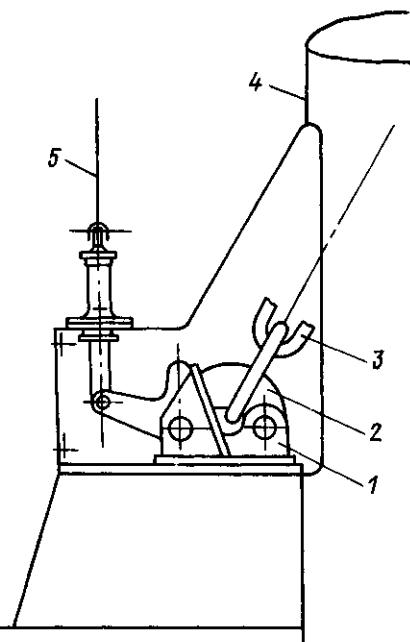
Приспособление для крепления и дистанционной отдачи коренного конца якорного каната
